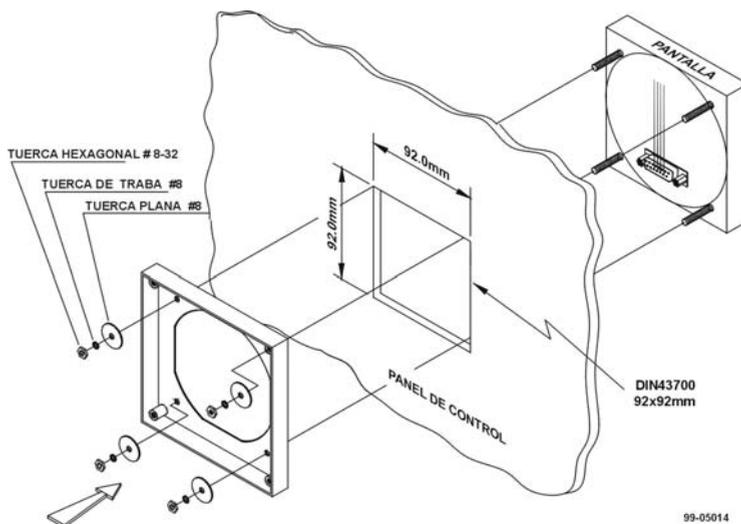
PASO 1 (92x92mm corte cuadrado DIN): Montar el módulo sobre el corte
